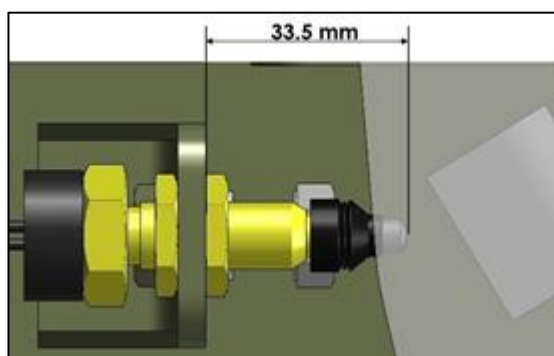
RÉGLAGE DU CONTACTEUR D'EMBAYAGE
